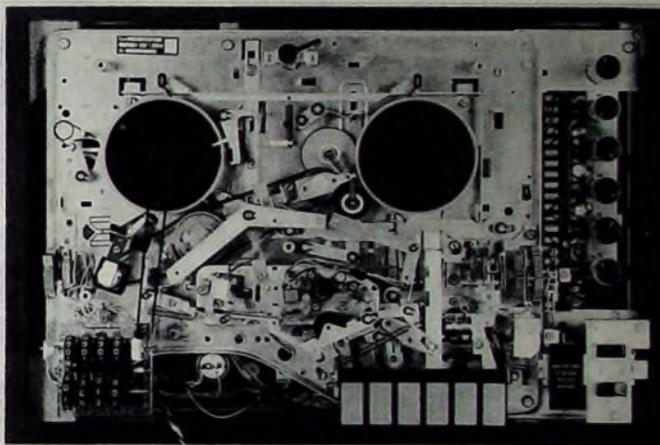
Blick auf das Chassis mit Kopfrägerplatte
